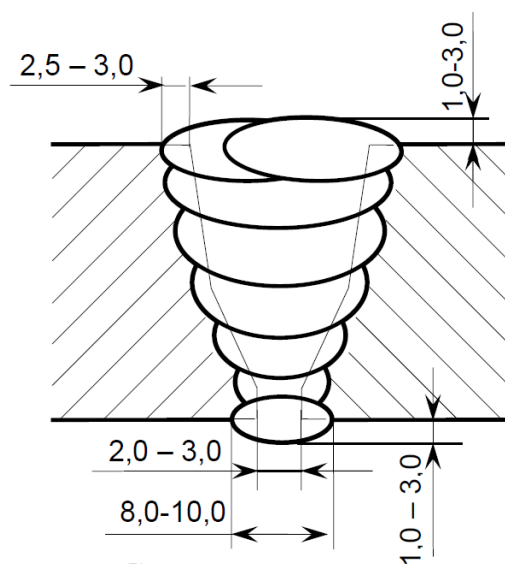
Геометрия сварного шва при выполнении неповоротного стыка труб механизированной сваркой самозащитной порошковой проволокой
